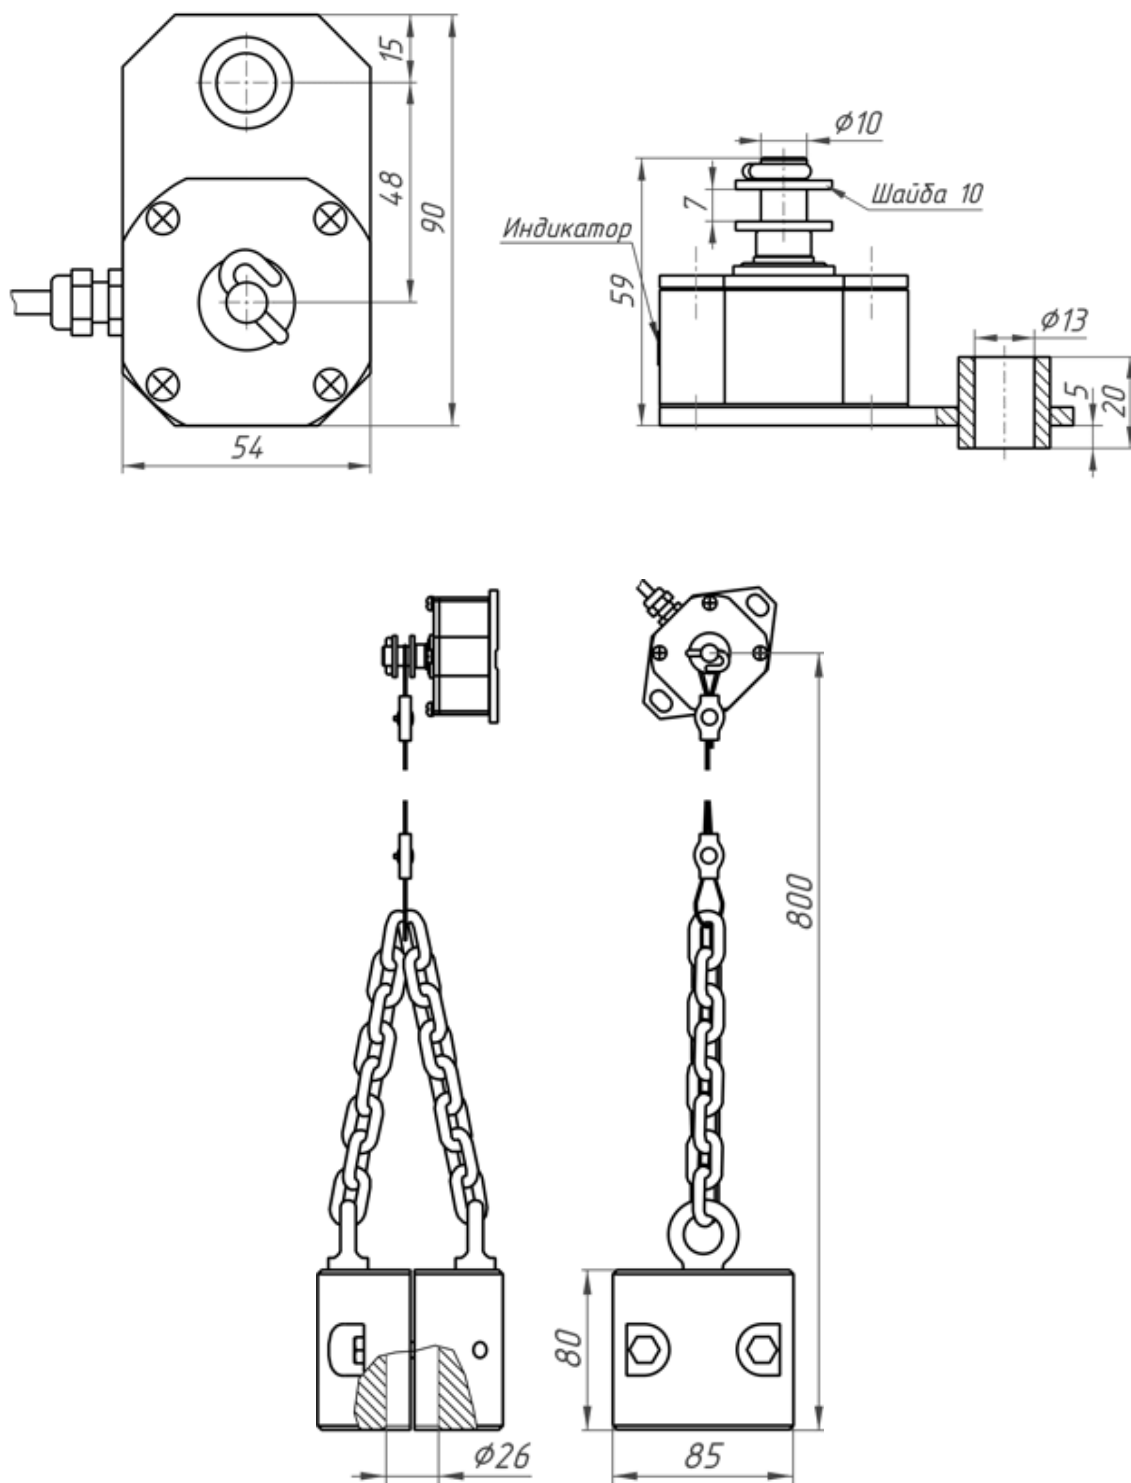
Габаритные размеры концевого выключателя ВМ
